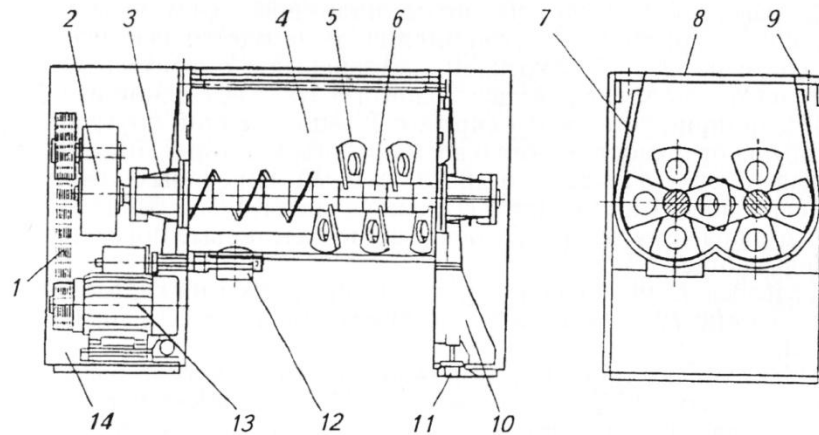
Смеситель SMKN с двумя горизонтальными валами
